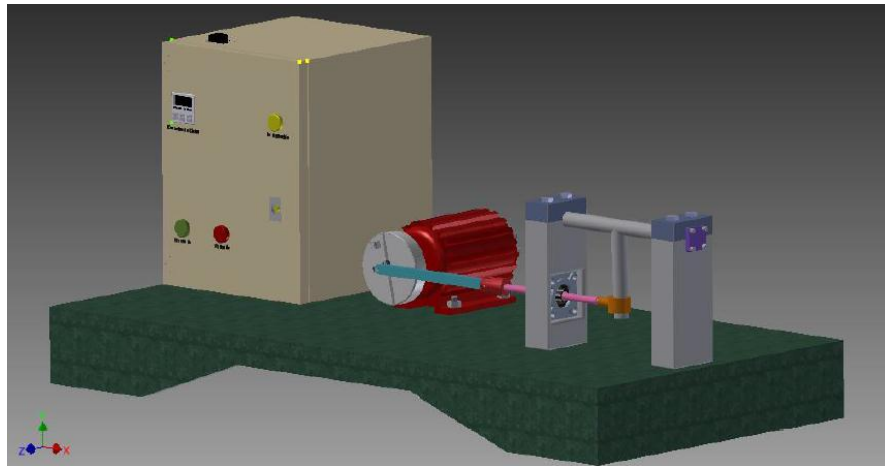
Máquina para pruebas de fatiga en uniones soldadas [4].
